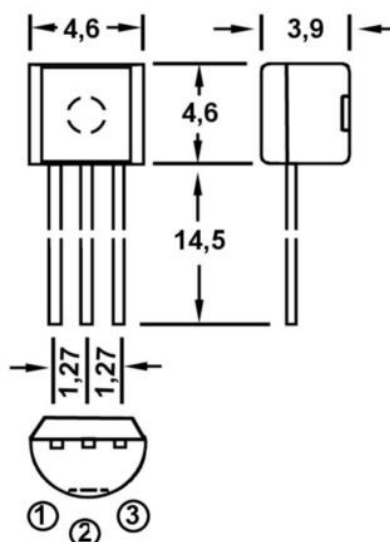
Габаритні розміри транзистора 2N3905
